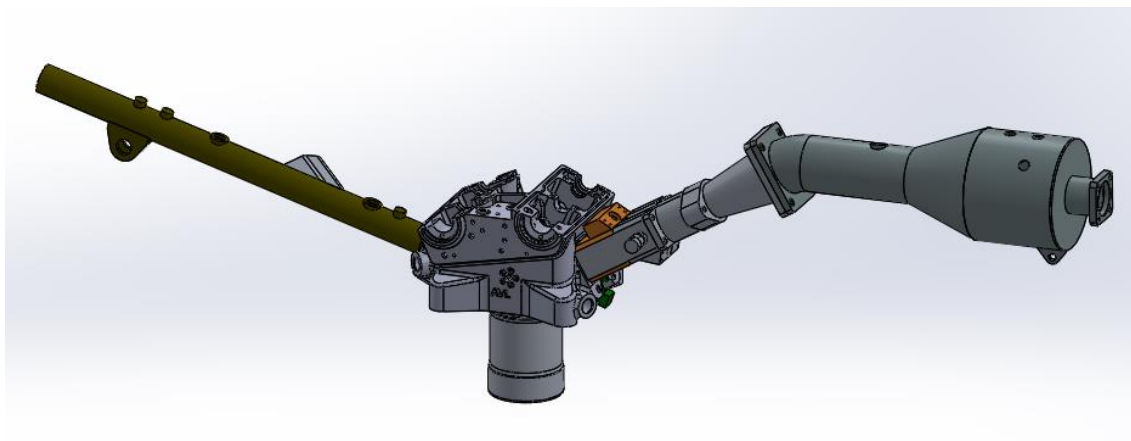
Montagem CAD do cabeçote e de parte dos dutos de admissão e exaustão. Fonte: Autor
